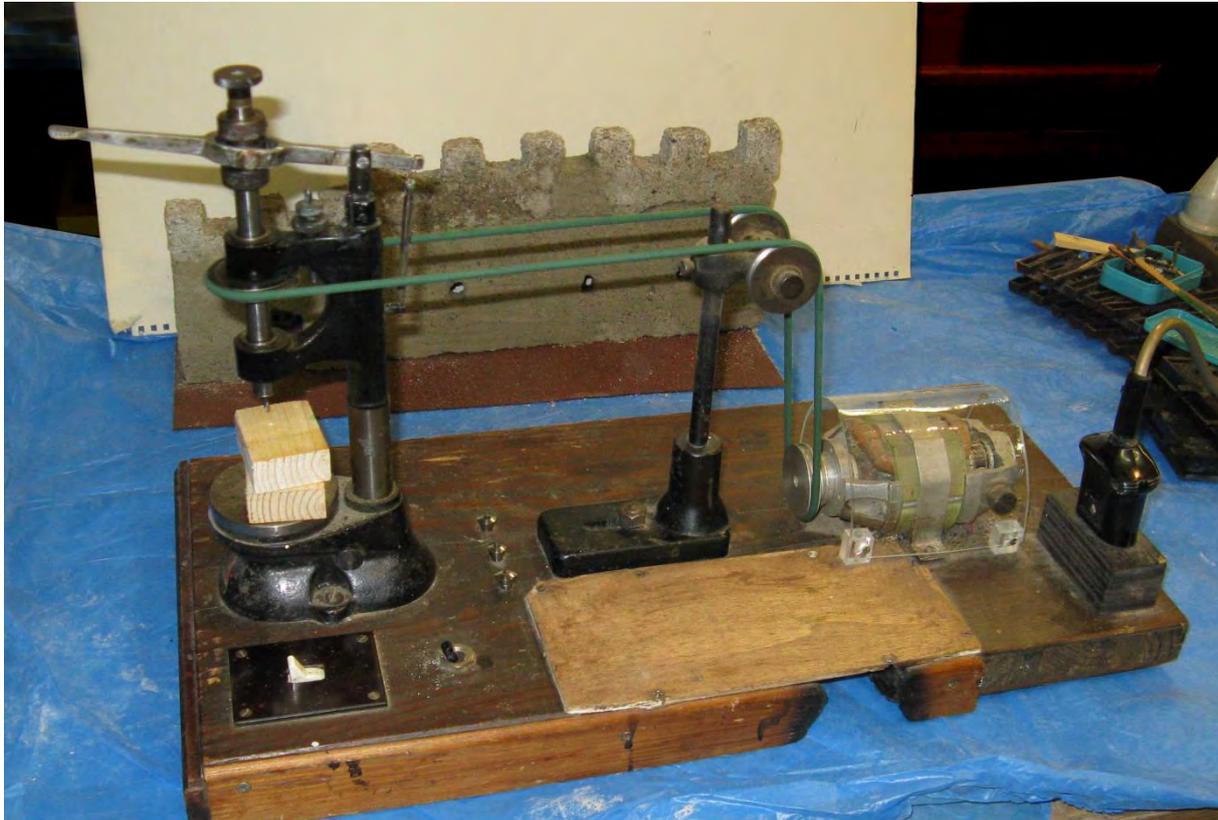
Mini-Ständerbohrmaschine mit Rundriemen
